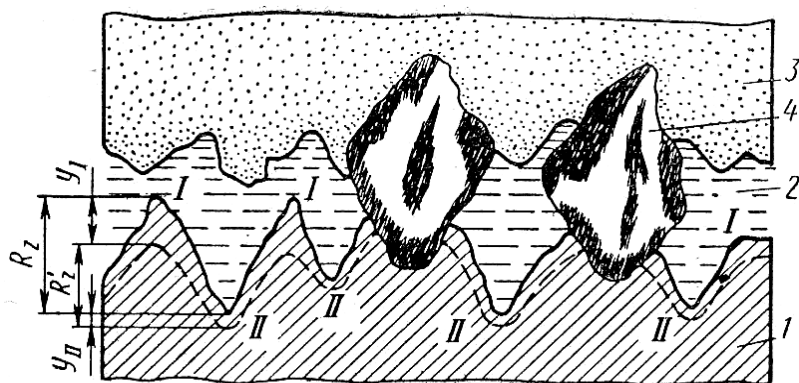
Схема формирований высоты шероховатости при электроабразивном шлифовании: 1 - обрабатываемая деталь; 2 - электролит; 3 – связка токопроводящего круга; 4 - абразивные зерна.
